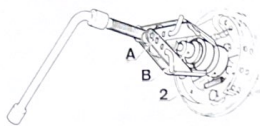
Forma de extraer del eje la pista del rodamiento.
